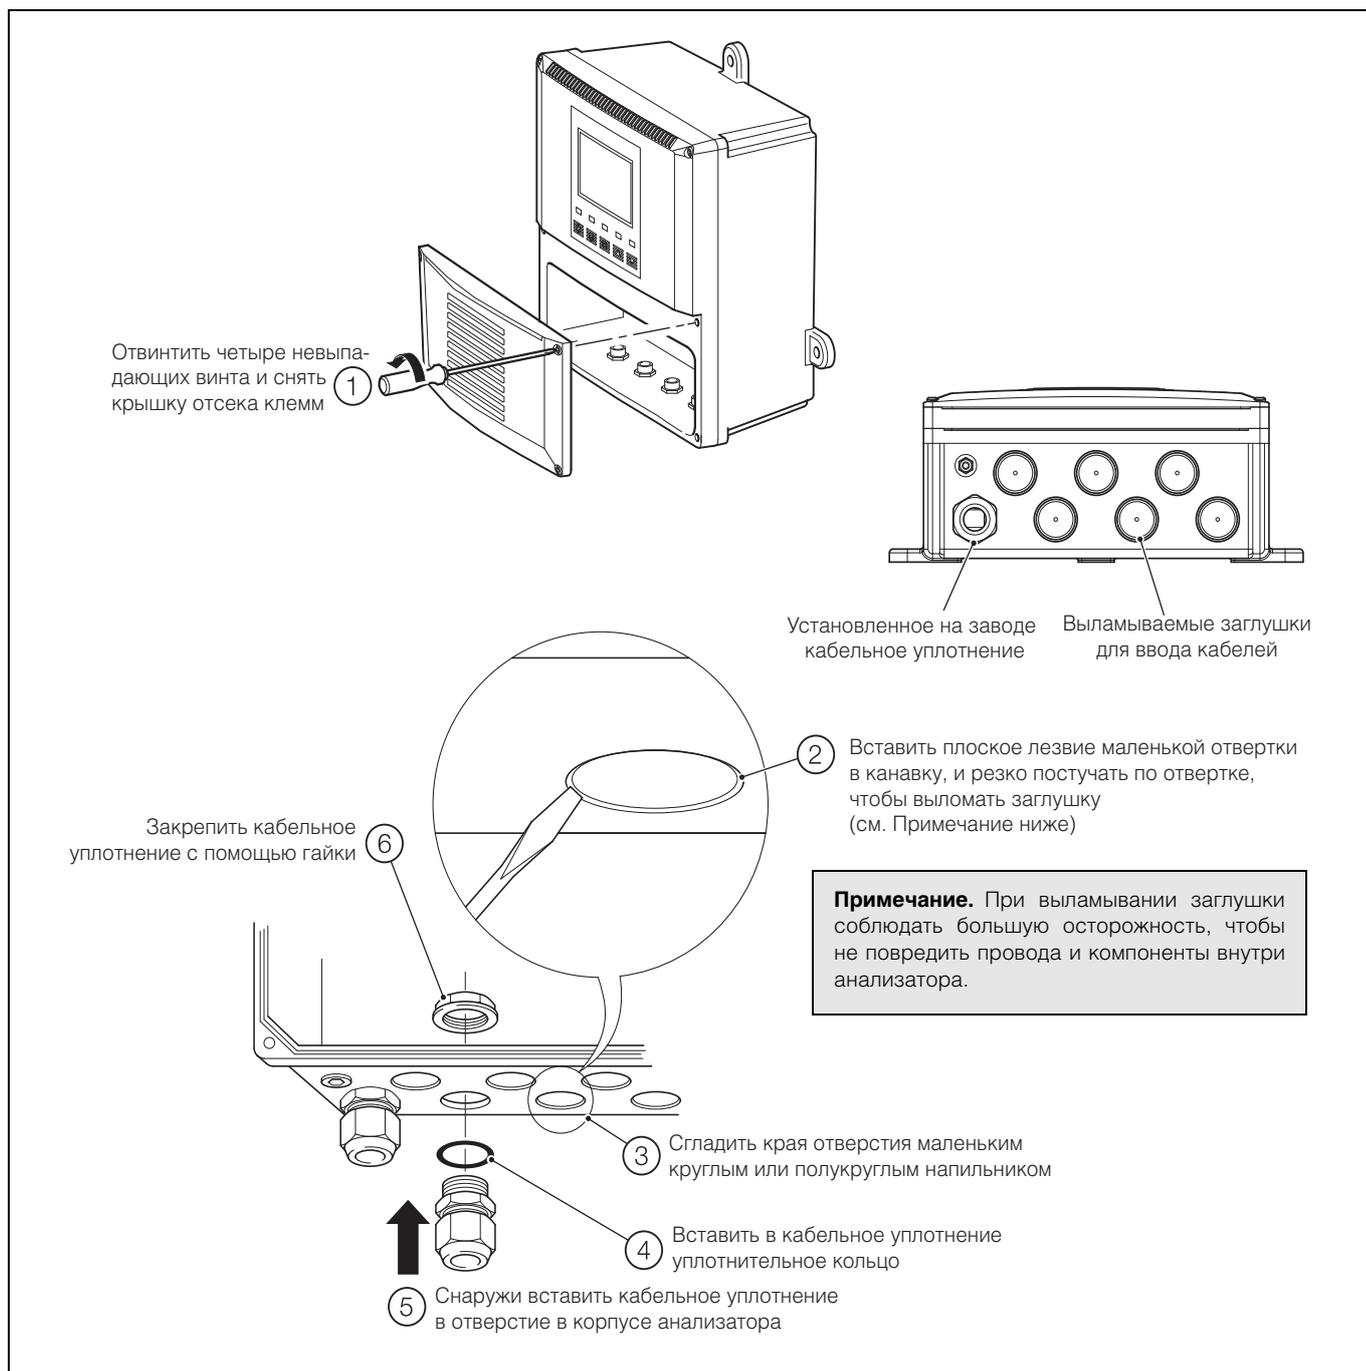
Выламываемые заглушки для ввода кабеля, анализатор настенного монтажа/монтируемый на трубе
